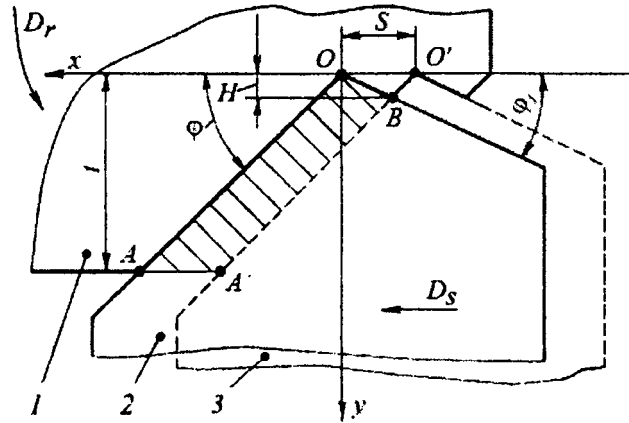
Схема несвободного резания резцом с незакругленной вершиной.
